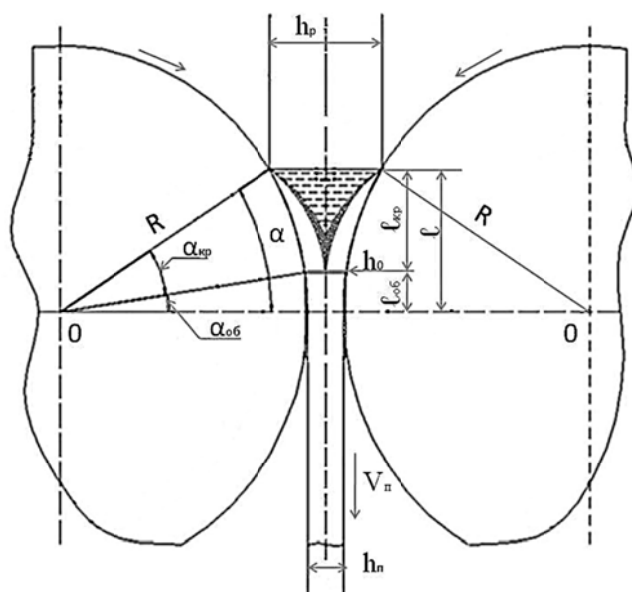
Схема поперечного сечения непрерывной валковой разливки-прокатки:
